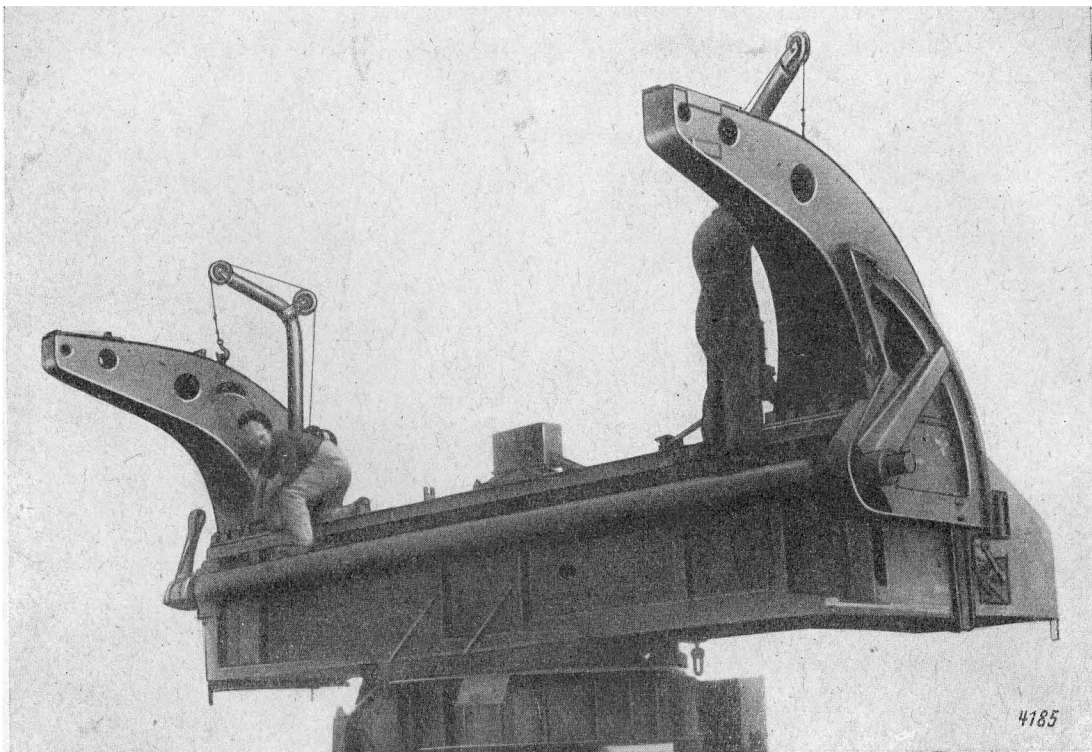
Tragarme auf den Hauptträger (III/3) niederlassen und die Befestigungsschrauben einführen. Mit Muttern leicht befestigen. Drahtseile lösen, Ausleger für die Schwenkkrane (IV/7) abnehmen und wegräumen, Paßbolzen einschlagen. Halteschrauben für die Tragarme anziehen.
